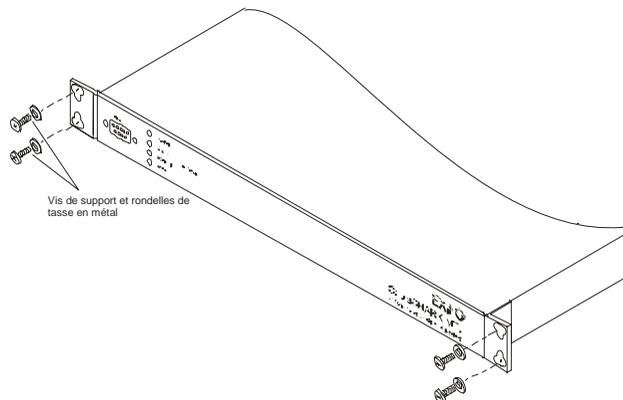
A – MONTAGE DU CABLESHARK MTU SUR UN BÂTI
